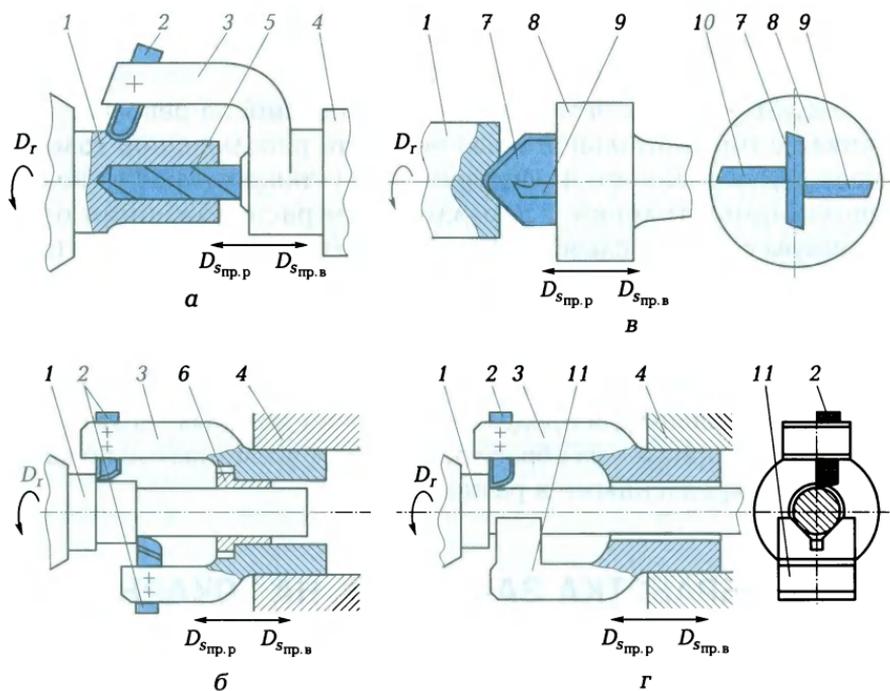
Упрощенные схемы обработки заготовок на револьверных станках:
